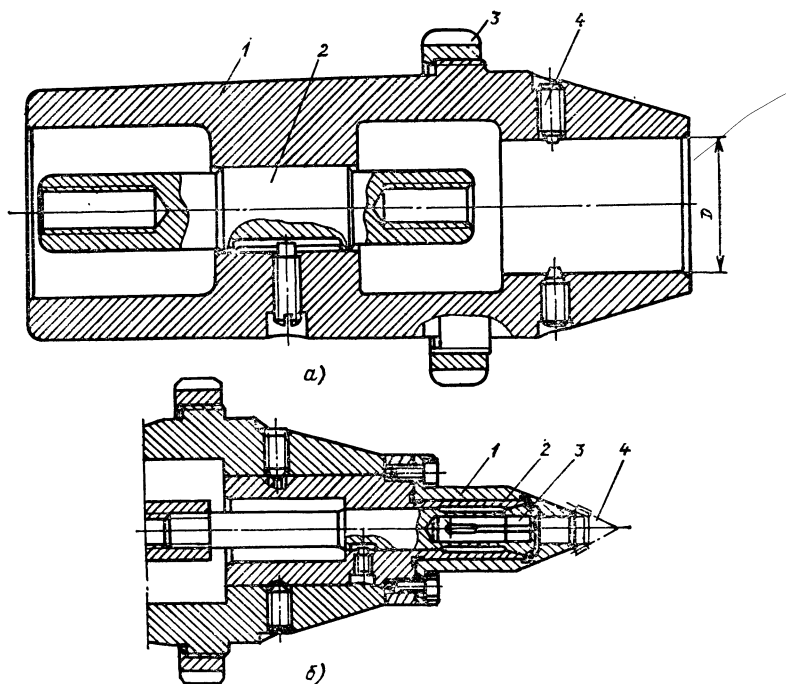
Переналаживаемые приспособления для обработки зубьев конических зубчатых колес на зубострогальных станках
